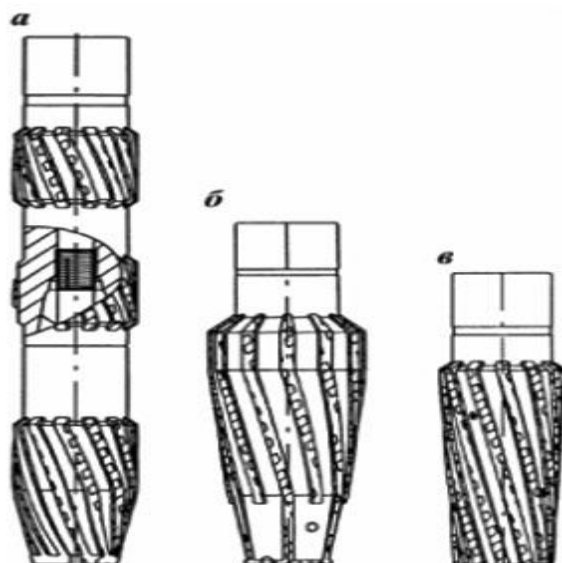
Типы фрезер-райберов: а – Тип ФРЛ; б – тип РПМ в – тип ФРС
